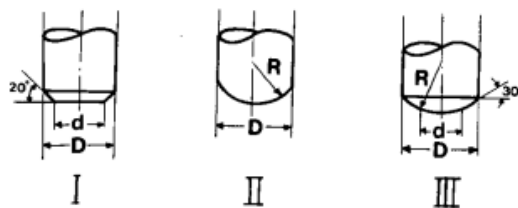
Geometrias dos eletrodos da soldagem por ponto.
